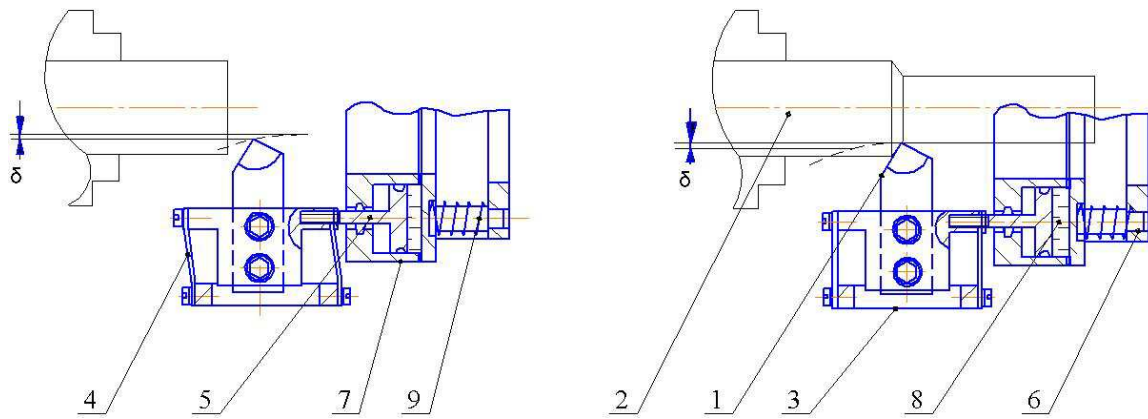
Принцип роботи багаторізевої головки з гідроприводом
